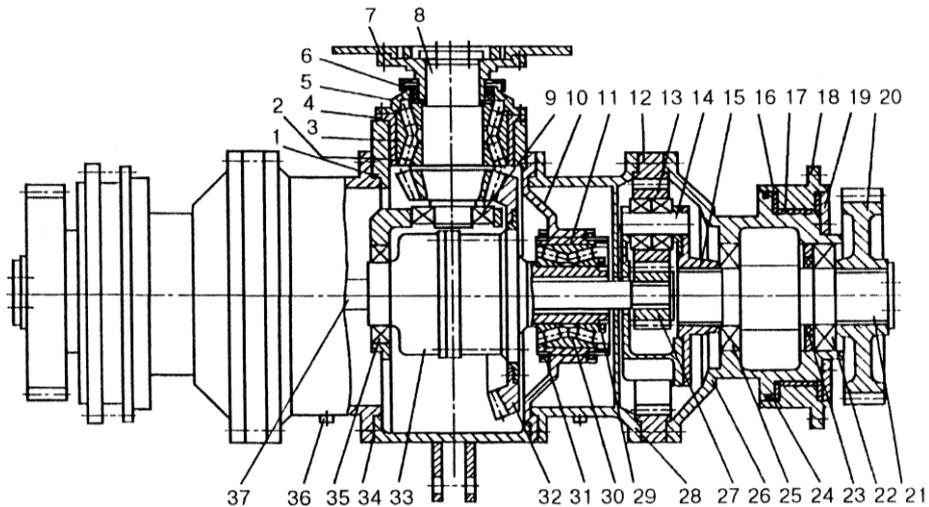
Центральный редуктор моста автогрейдера А120: 1 – корпус; 2, 11 – стаканы; 3, 30 – конические подшипники; 4 – регулировочная прокладка; 5 – крышка; 6, 23 – манжеты; 7, 15, 18 – фланцы; 8 – ведущая шестерня; 9 – роликовый подшипник; 10 – вставка; 12, 13, 20, 27 – шестерни; 14 – ось; 16 – кольцо; 17 – втулка; 19 – диск; 21 – вал; 22, 25, 35 – подшипники; 24 – уплотнение; 26 – ступица; 28 – переходник; 29, 31 – гайки; 32 – ведомая шестерня; 33 – дифференциал; 34 – прокладка; 36 – пробка; 37 – полуось
